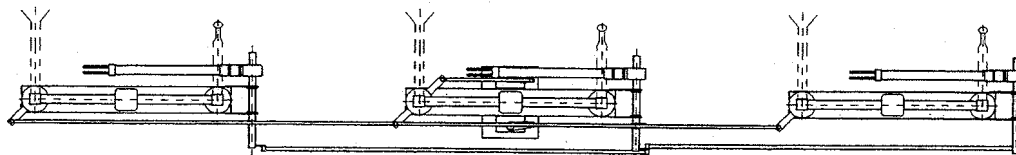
3-полюсной двухколонковый поворотный разъединитель типа SGF при последовательном расположении полюсов.
